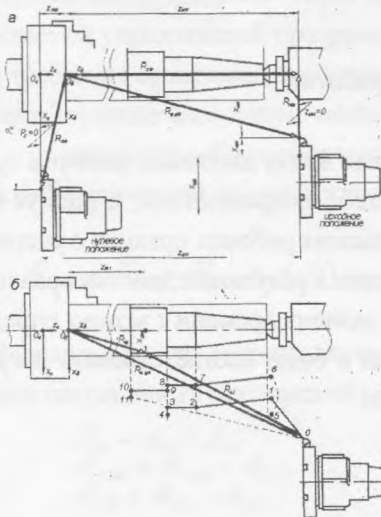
Статическая настройка токарного станка с устройством ЧПУ
